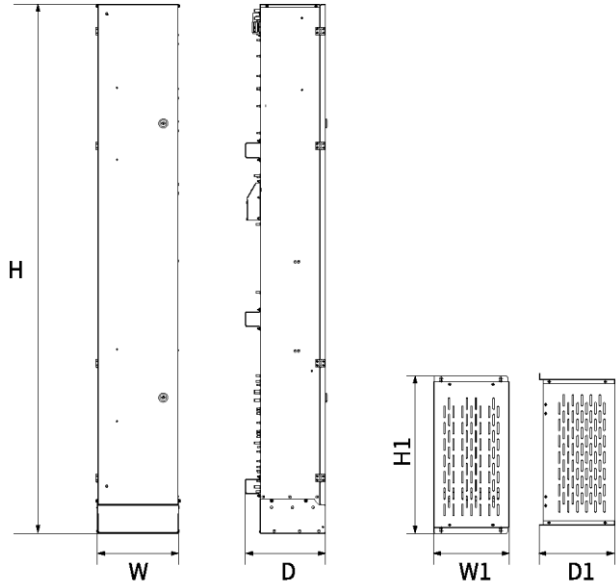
Размеры шкафа управления пожарного лифта
